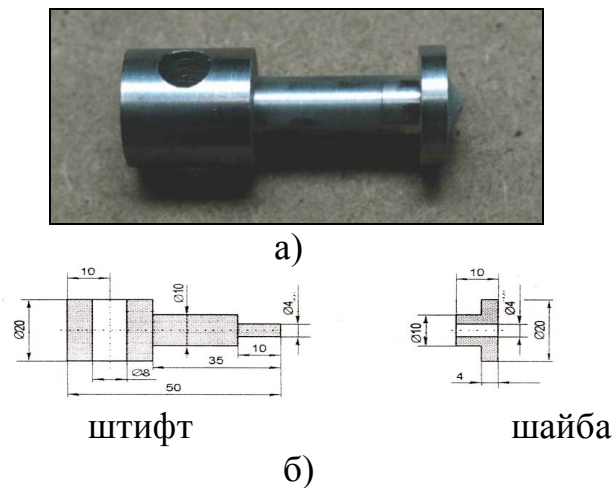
Общий вид образца для определения прочности сцепления покрытий, полученных ГДН: а) образец в сборе; б) составные части образца.
